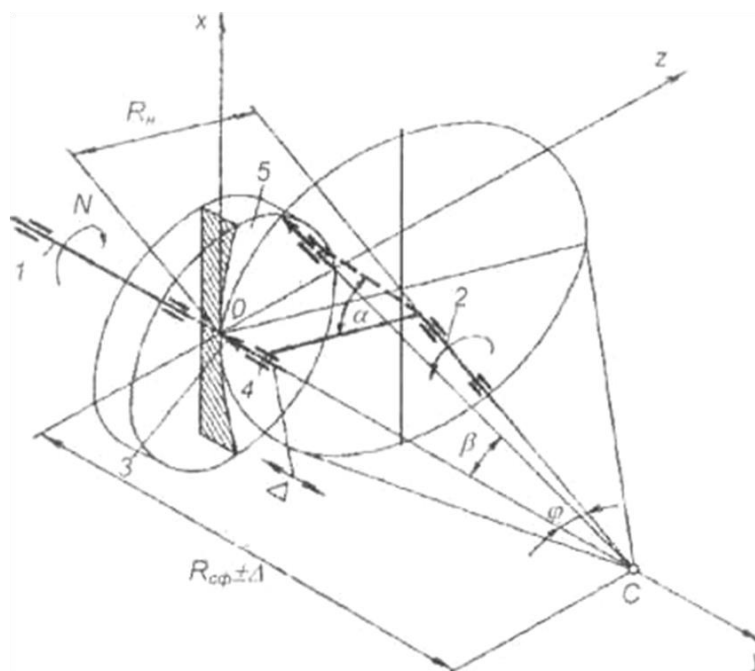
Схема обработки асферического зеркала на верстаті САТ-1808:
